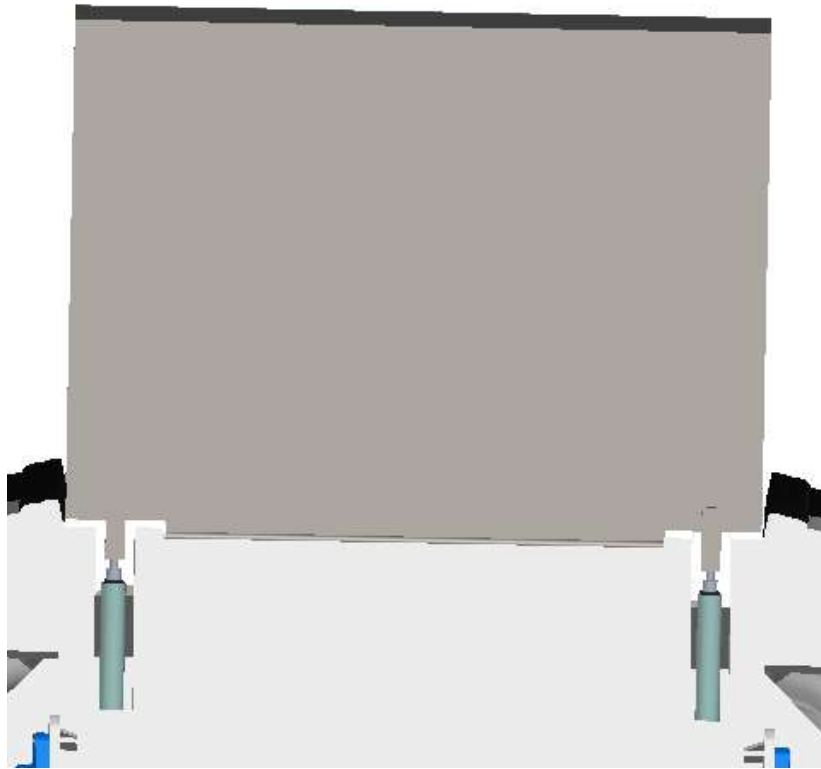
Sistema de apertura de puerta inferior con pistón de elevación. Fuente: (Vaca, José, 2018)
